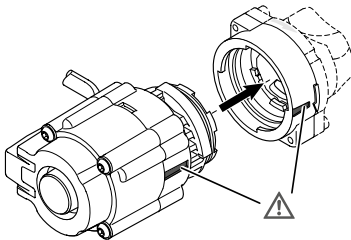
Heatfixx-Pumpe auf Pumpenadapter aufstecken
